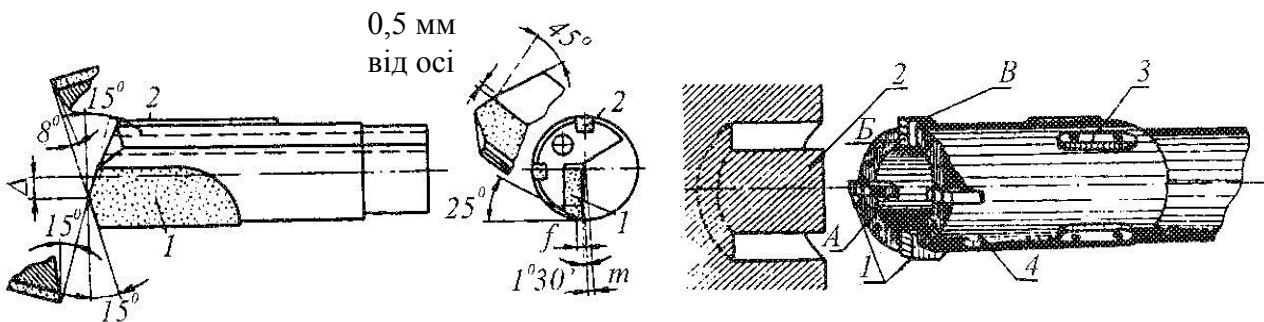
Свердло ружейне з припаяною пластинкою з твердого сплаву
